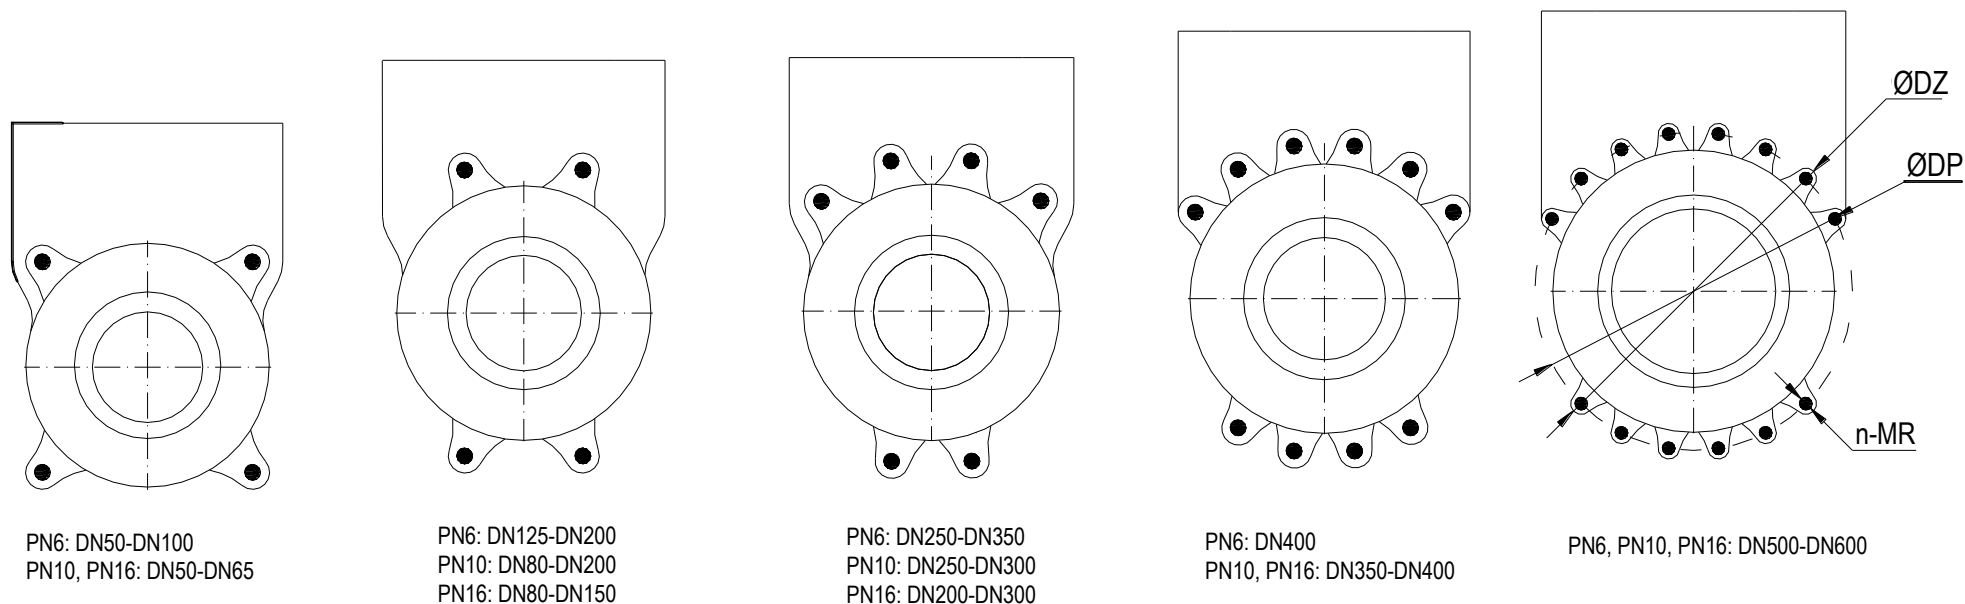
Główne wymiary urządzenia | Main device dimensions | Основные размеры устройства
